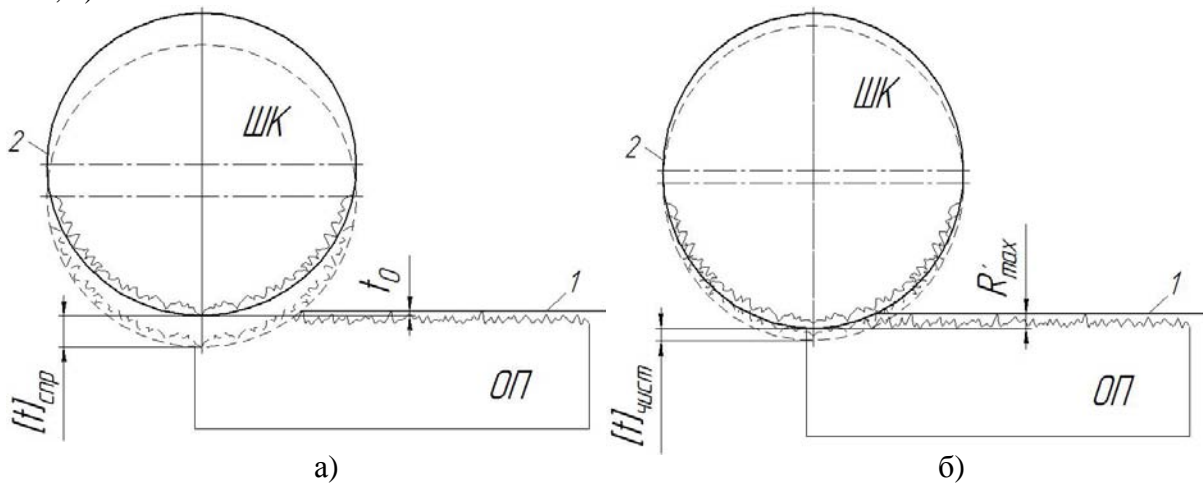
Схема снятия припуска при черновой и чистовой стадиях обработке
